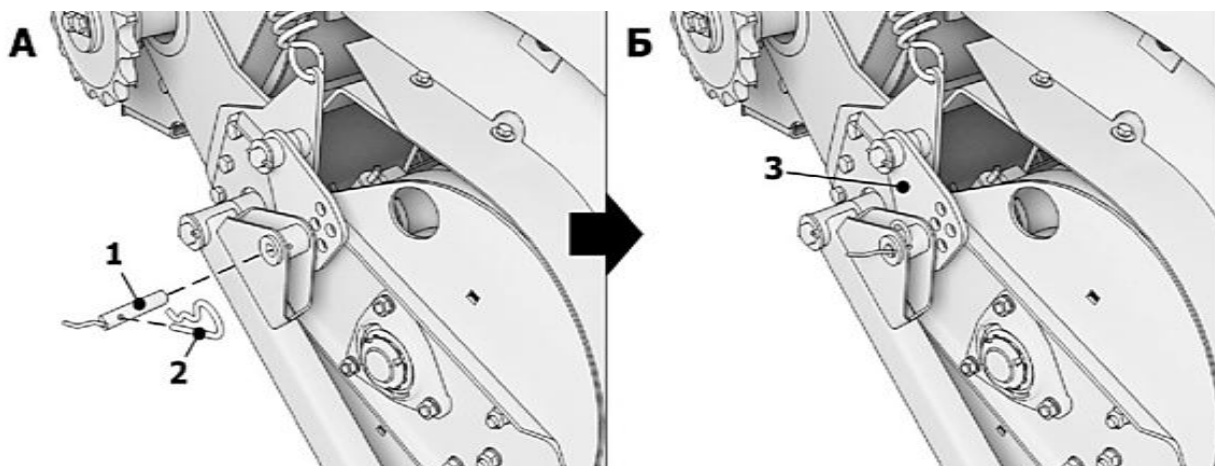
Установка опорного колеса подборщика: 1 – штырь фиксации; 2 – шплинт; 3 – поворотная планка
